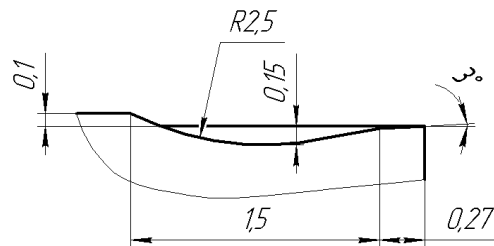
Геометричні параметри вершини корегованої пластини
